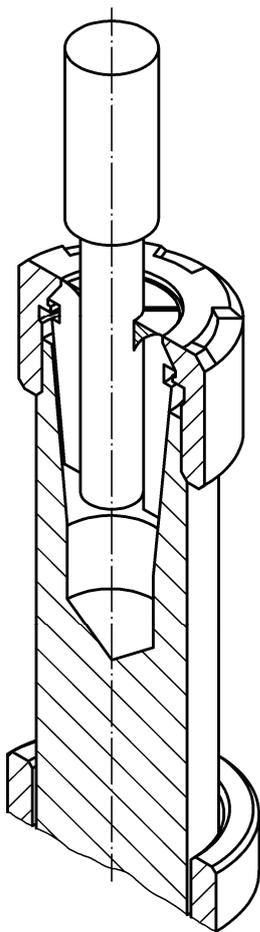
Beispiel für eine Spindel für Schaftwerkzeuge
